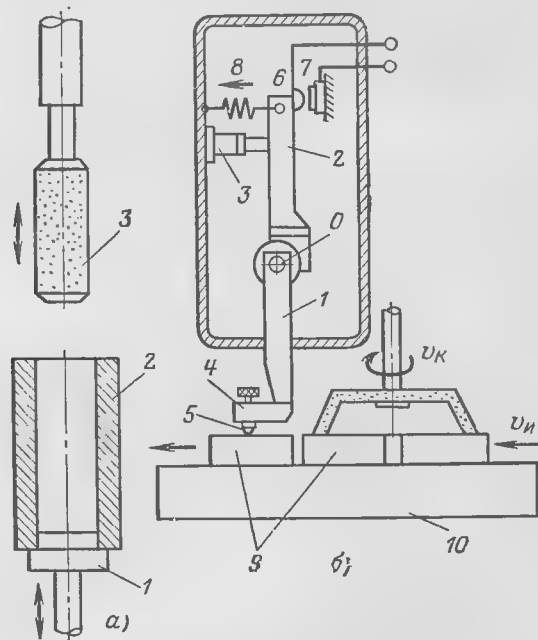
Механические устройства для контроля размеров при шлифовании.
